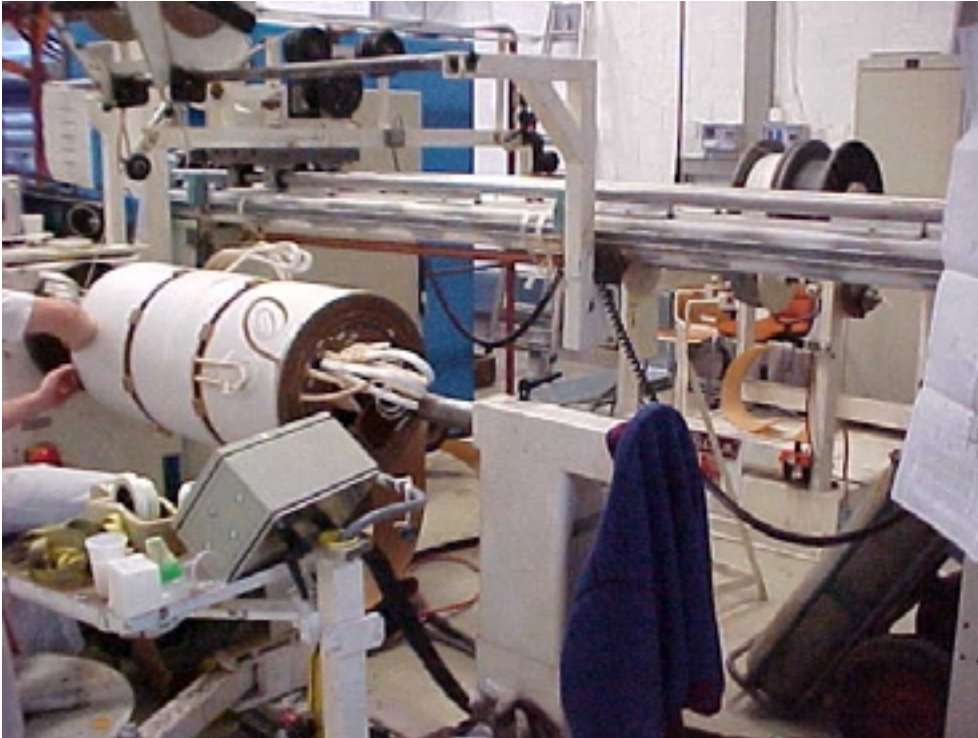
tour de bobinage rallongé spécialement pour le bobinage du prototype
